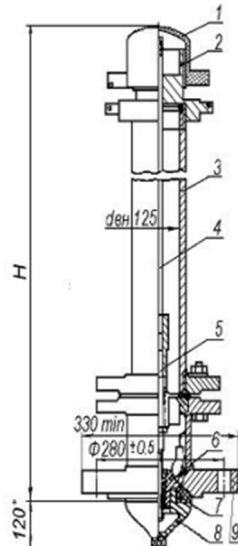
Схема улаштування пожежного гідранту підземного типу: 1 – кришка (поліетилен); 2 – ніпель (бронза); 3 – корпус (сталь); 4 – штанга (сталь); 5 – шпіндель (нержавіюча сталь); 6 – корпус клапана (бронза); 7 – кільце; 8 – гайка клапана (чавун); 9 – патрубок (чавун)
